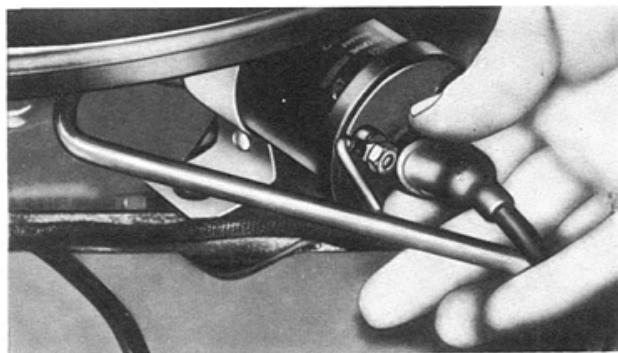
Instalação do Cabo Secundário e Protetor na Bobina
